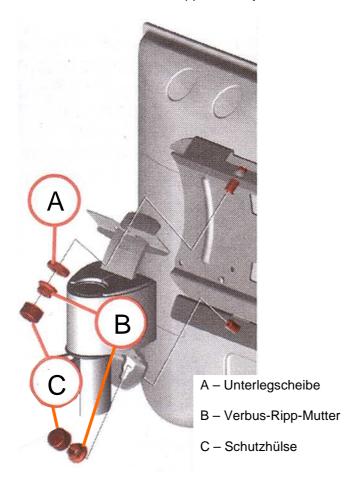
Detail-Rückansicht Displayhalterung an der Wandhalterung befestigen
